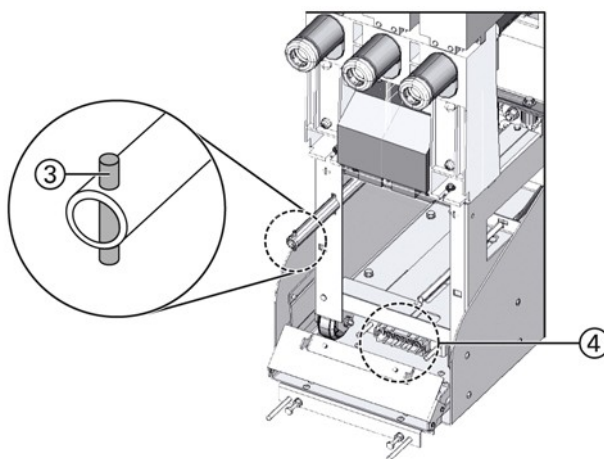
Соединительная шпилька вала привода ножа заземления.
